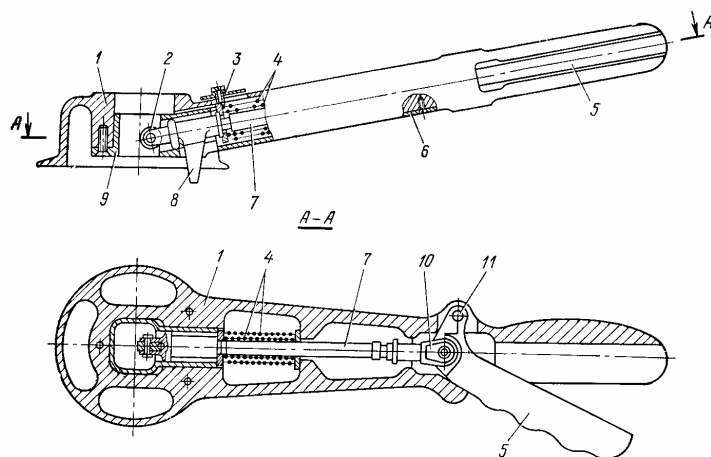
Внутренняя ручка: 1—корпус; 2—ролик; 3—скоба; 4—пружин стопора; 5—рычаг (гашетка); 6—крышка; 7—тяга; 8—стопор; 9—вставка; 10—вилка; 11—ось гашетки
